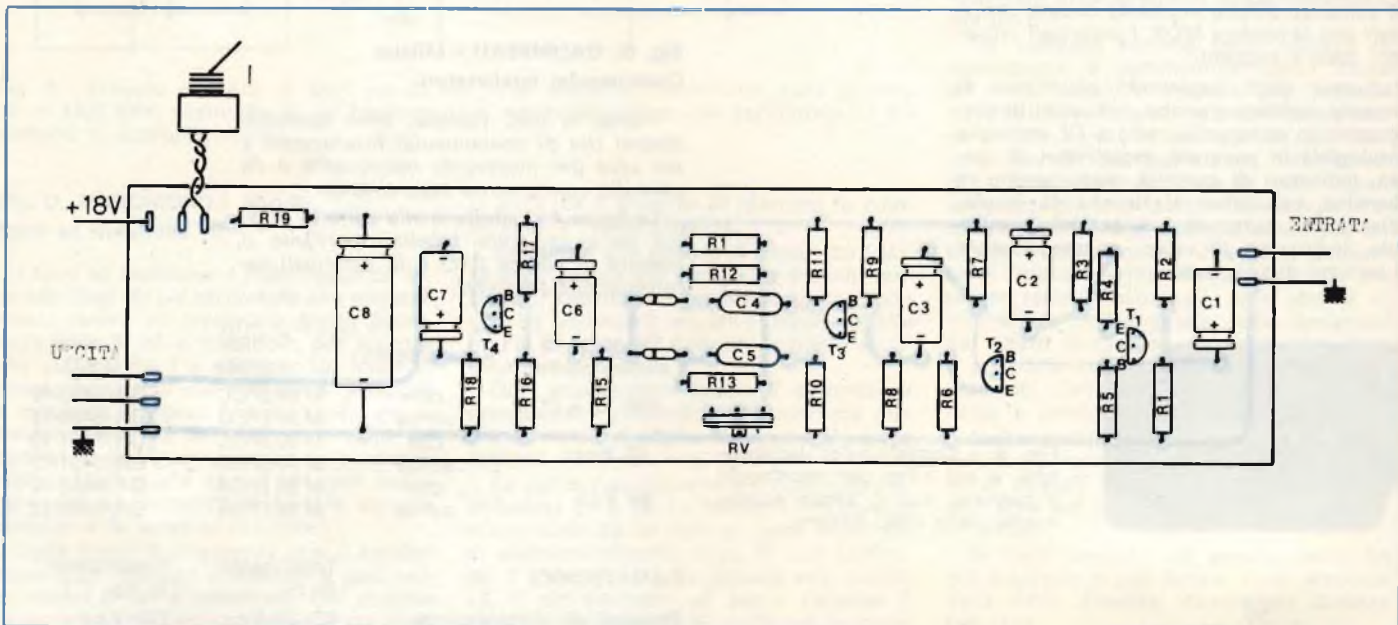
Circuito stampato del dispositivo di cui alla figura 8, visto dal lato componenti.
